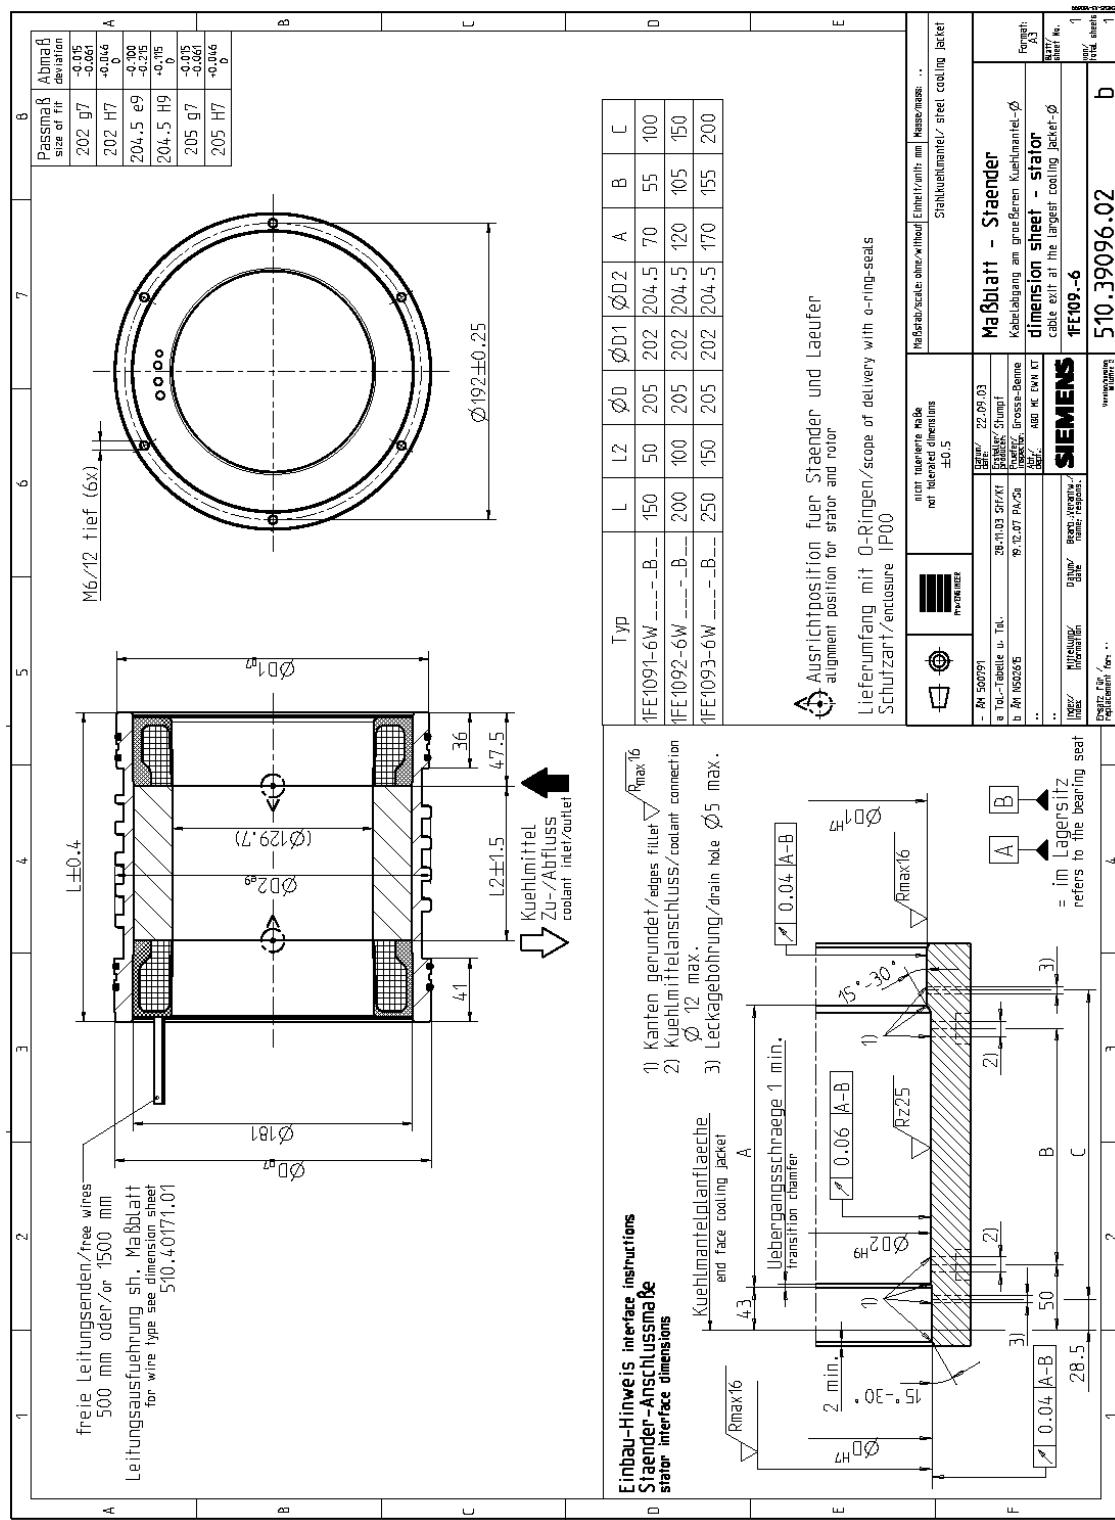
1FE109□-6, Ständer mit Kühlmantel, Kabelabgang am größeren Kühlmanteldurchmesser
